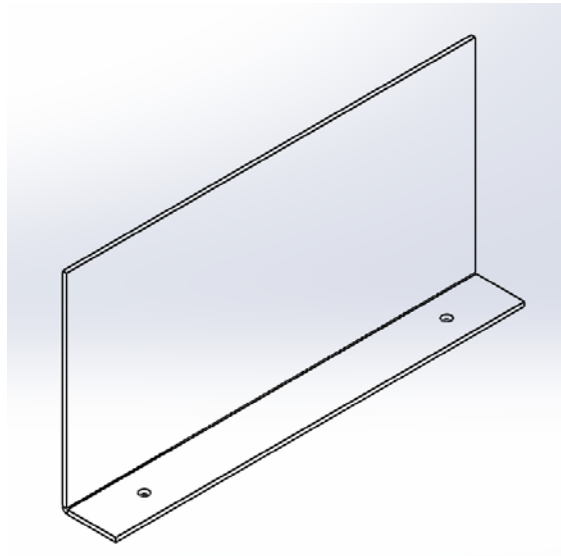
Chapa soporte tanque (2 piezas)
